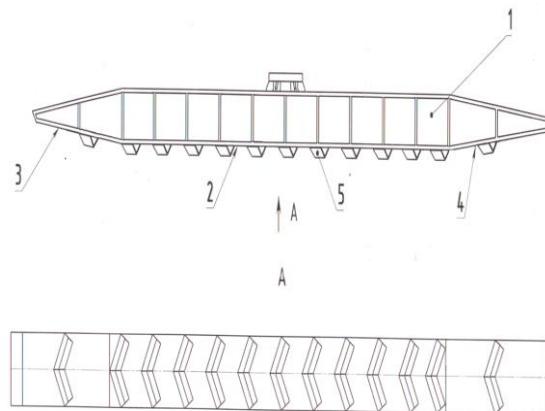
Вдосконалена конструкція опорної поверхні лиж крокуючого екскаватора: 1-корпус; 2- горизонтальна поверхня; 3,4 - похила поверхня; 5- опорний елемент лижі.
